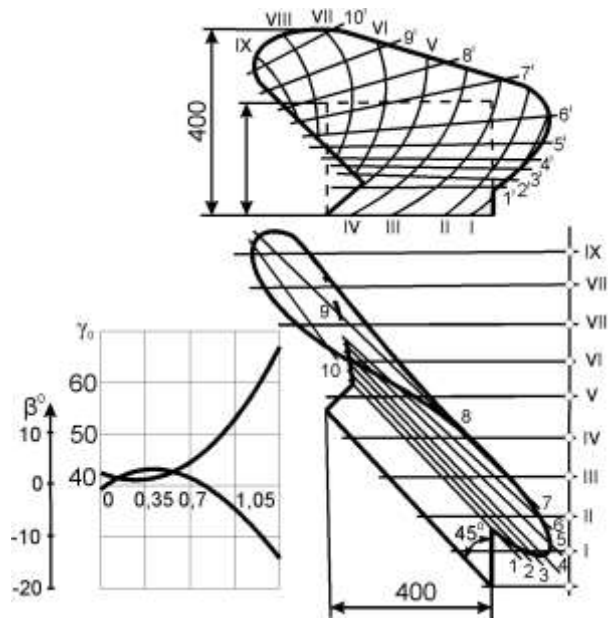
Поверхня напівгвинтового корпусу верхнього ярусу двох'ярусного плуга ПНЯ-4-40.
